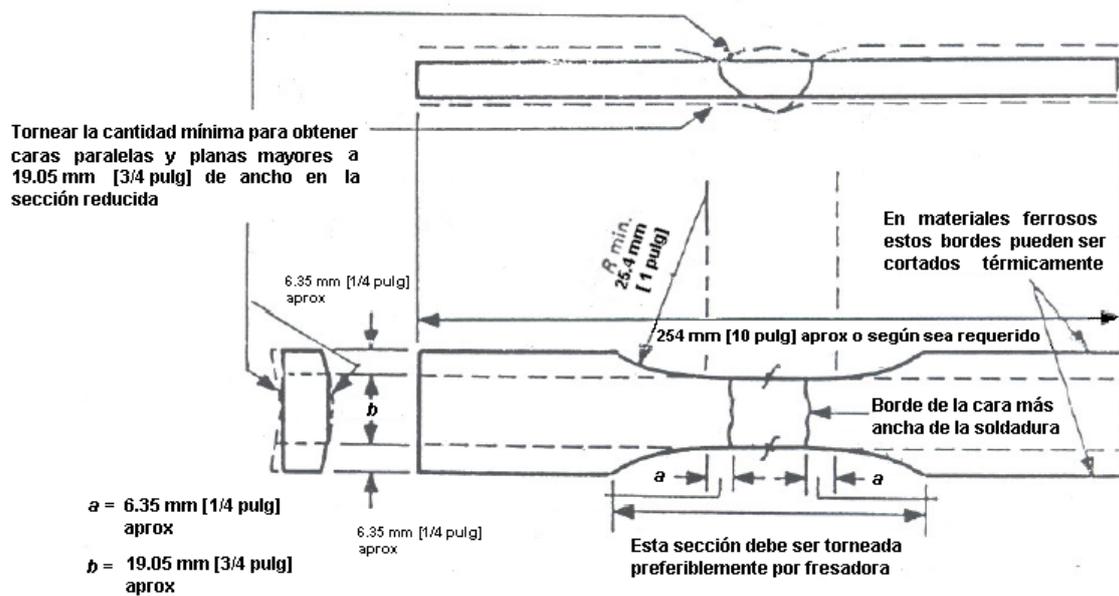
Probeta de acero soldada obtenida de un tubo.
